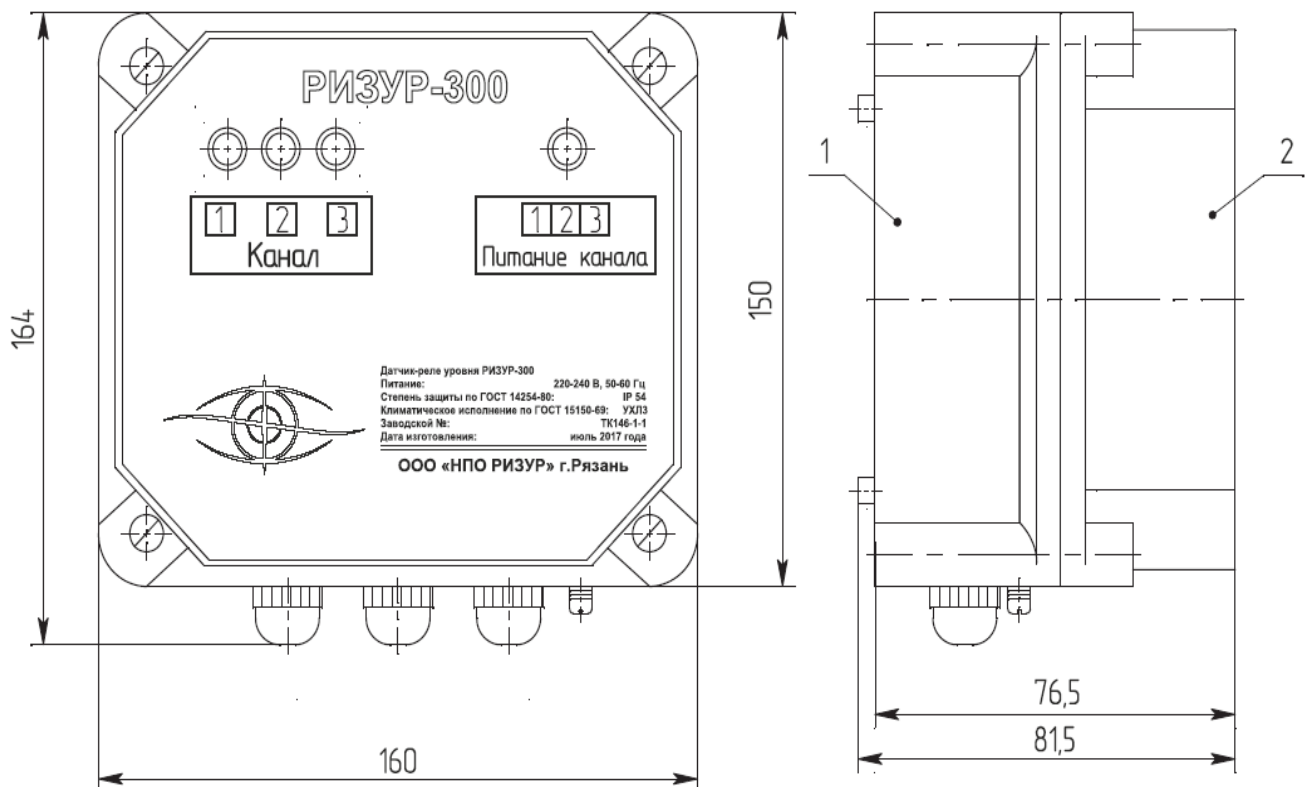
Габаритные размеры для 1-3 датчика
